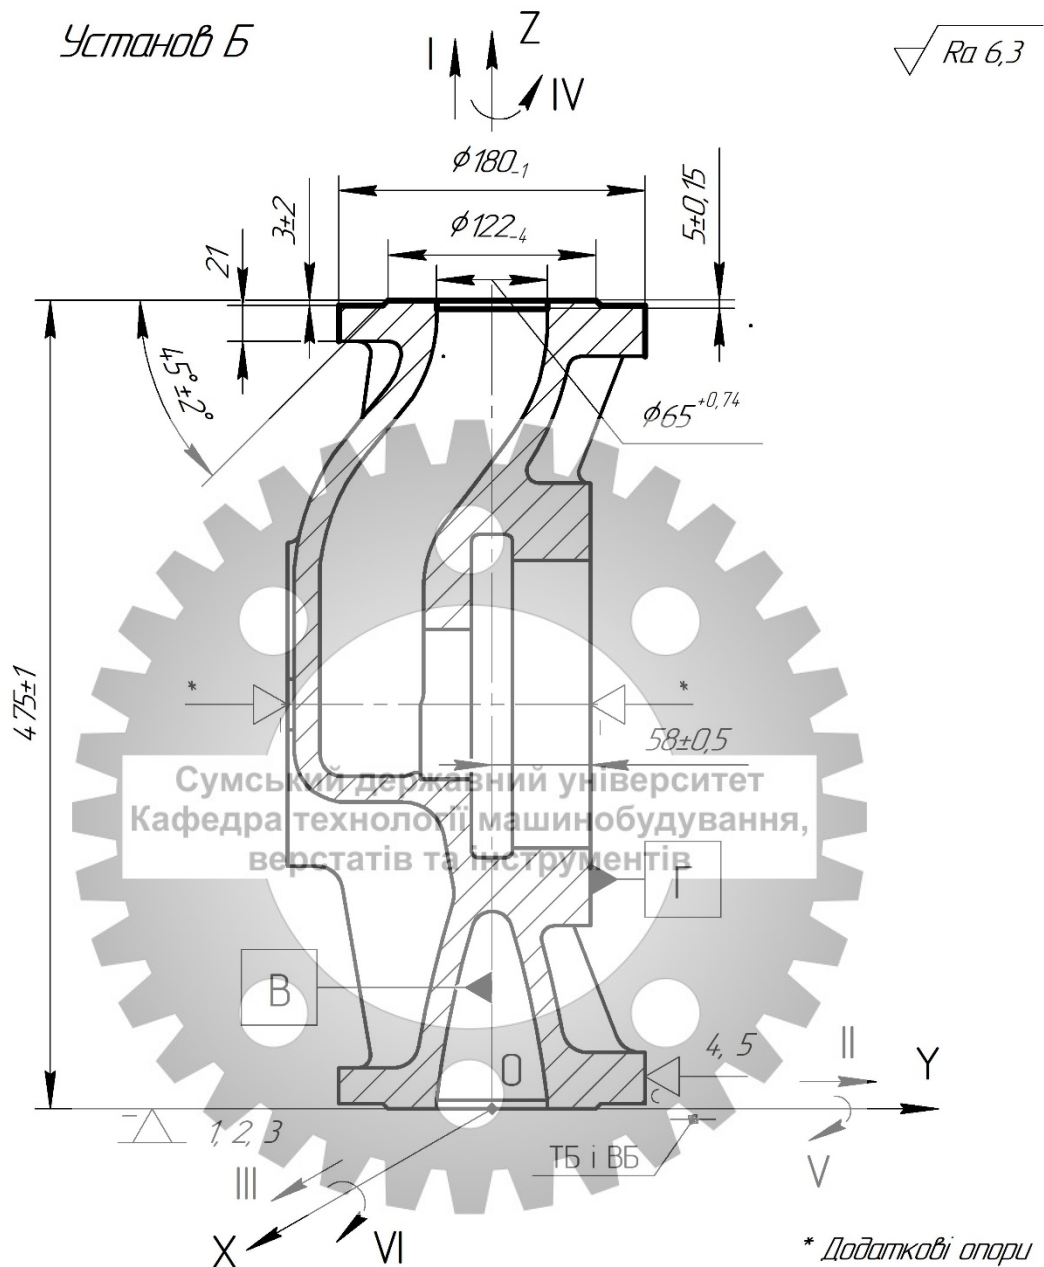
Схема установлення заготовки на операції 015. Варіант 2
